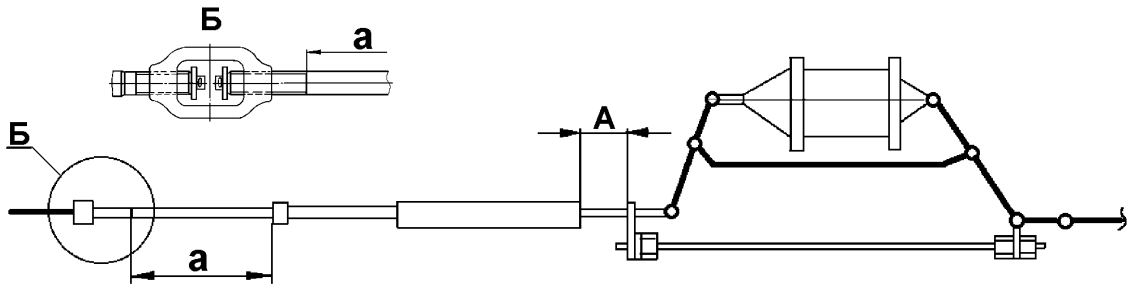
Схема установки на вагоне регулятора тормозной рычажной передачи со стержневым приводом
